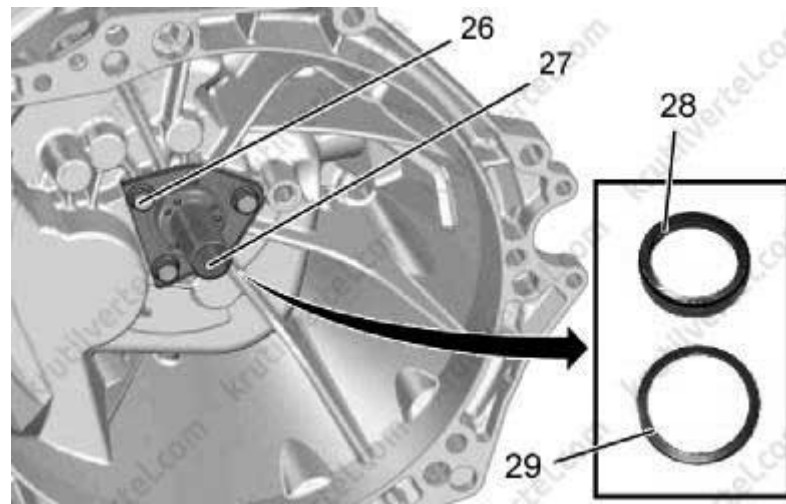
Зняття направляючої втулки вижимного підшипника
